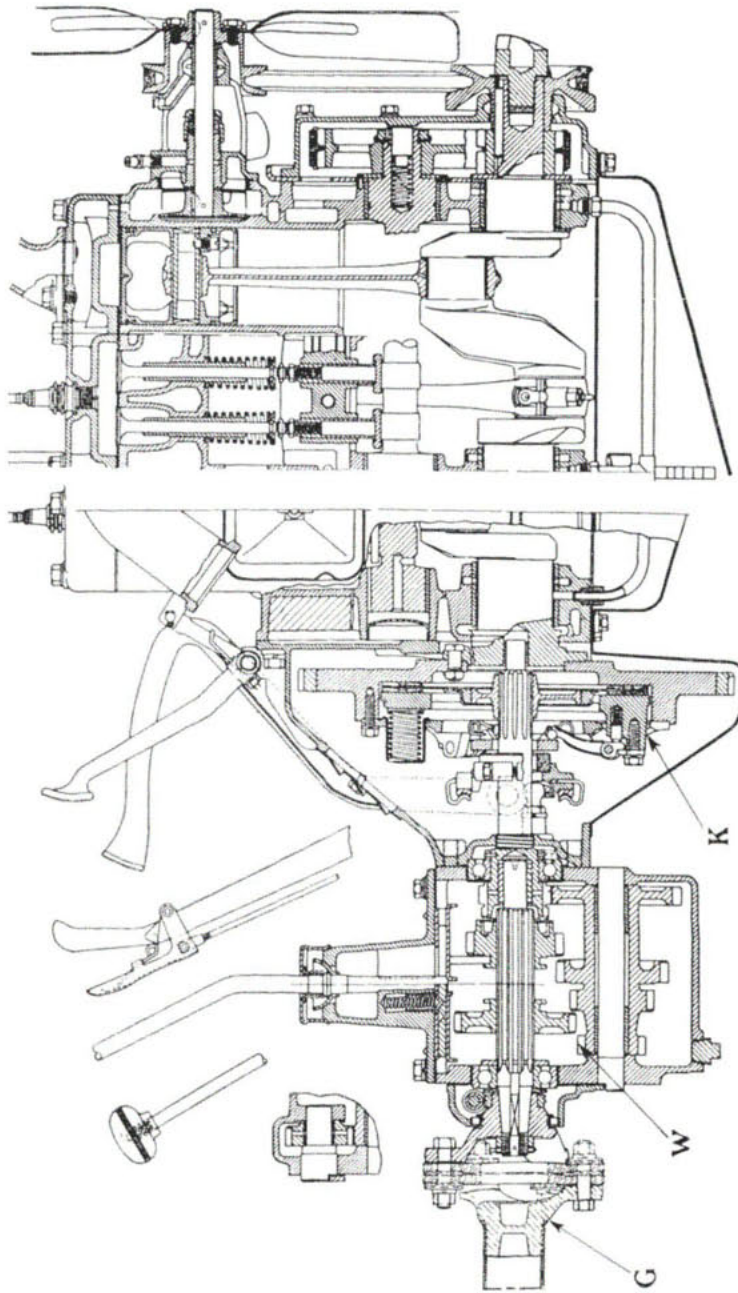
Längsschnitt durch Motor, Kupplung und Getriebe.
